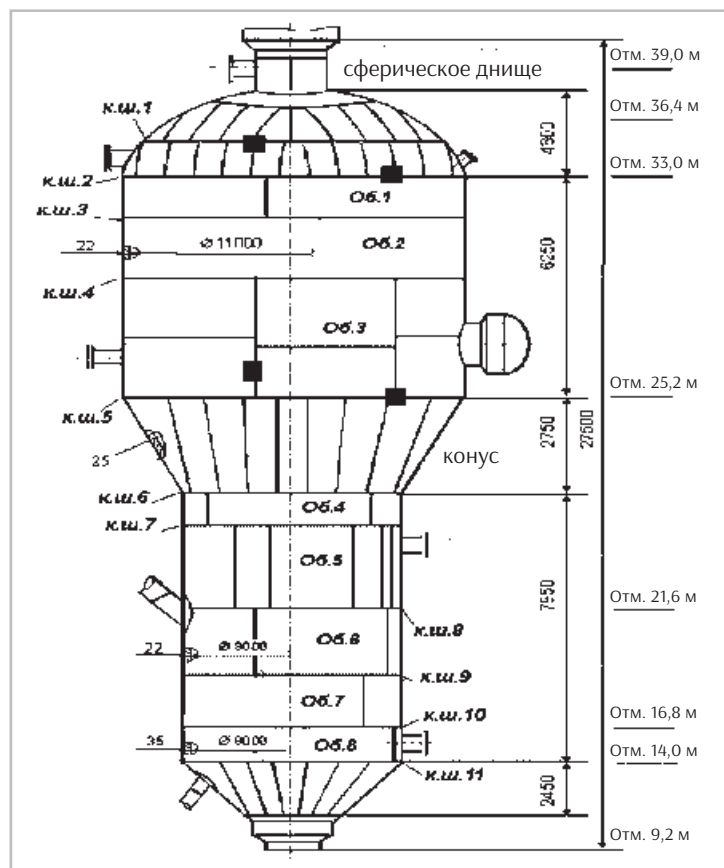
Схематическое изображение корпуса регенератора Р-202
